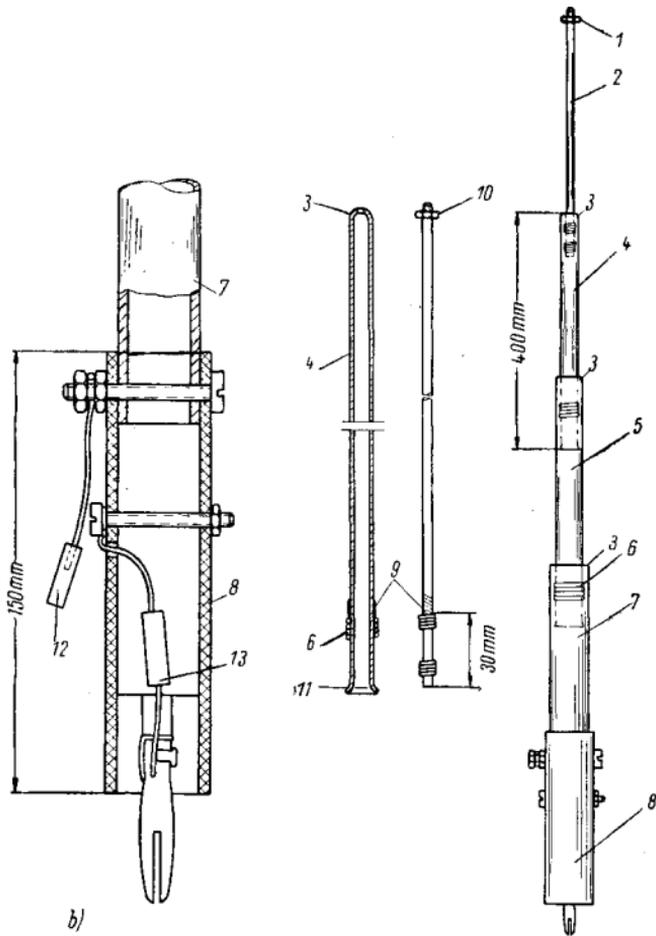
b) ausziehbare Hilfsantenne aus Metallrohren; 1 — Spitze, mit 3-mm-Gewinde versehen und Mutter aufgeschraubt; 2 — Automatenstahl, 3 mm Dmr.; 3 — Rohre nach innen gebördelt; 4 — Messingrohr, 5×0,5 mm; 5 — Messingrohr, 7×0,5 mm; 6 — aufgebrachte Drahtwindungen; 7 — Messingrohr 10×1 mm; 8 — Vinidurrohr; 9 — leichter Zinnüberzug zum Festklemmen; 10 — Mutter M 3; 11 — Rohr, nach außen aufgetrieben auf Innendurchmesser des folgenden Rohres; 12 — Schalter aus Federdraht; 13 — 10-k $\Omega$ -Widerstand
